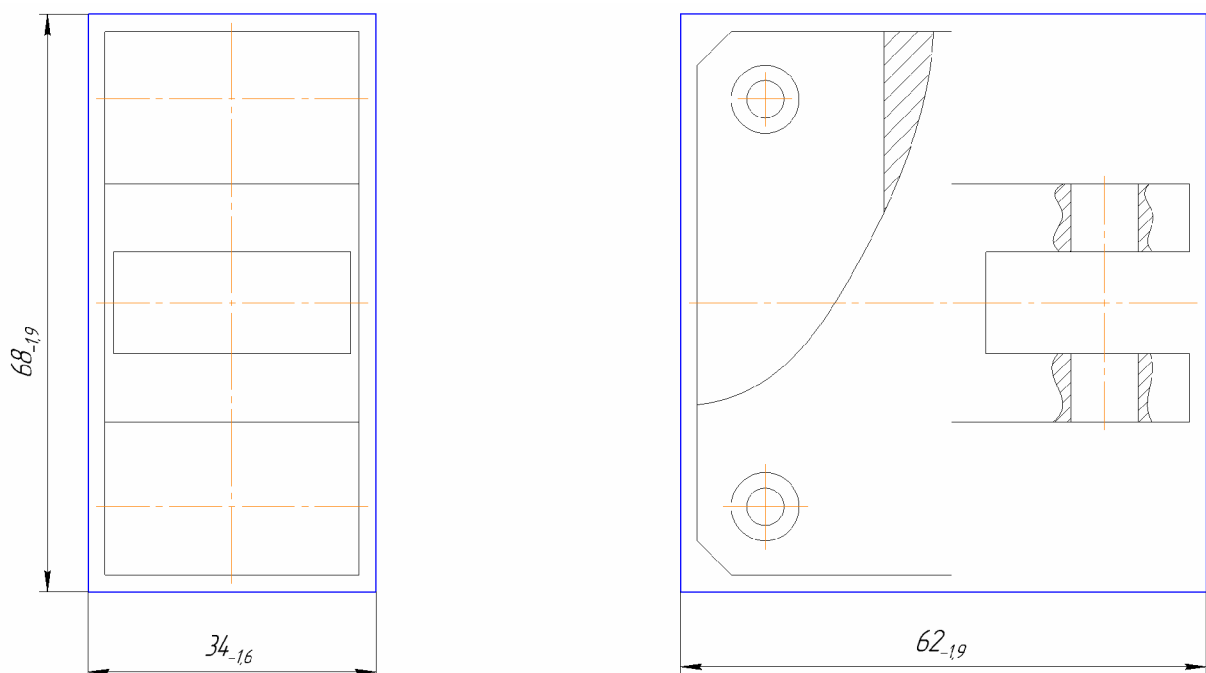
Ескіз заготовки деталі Корпус
